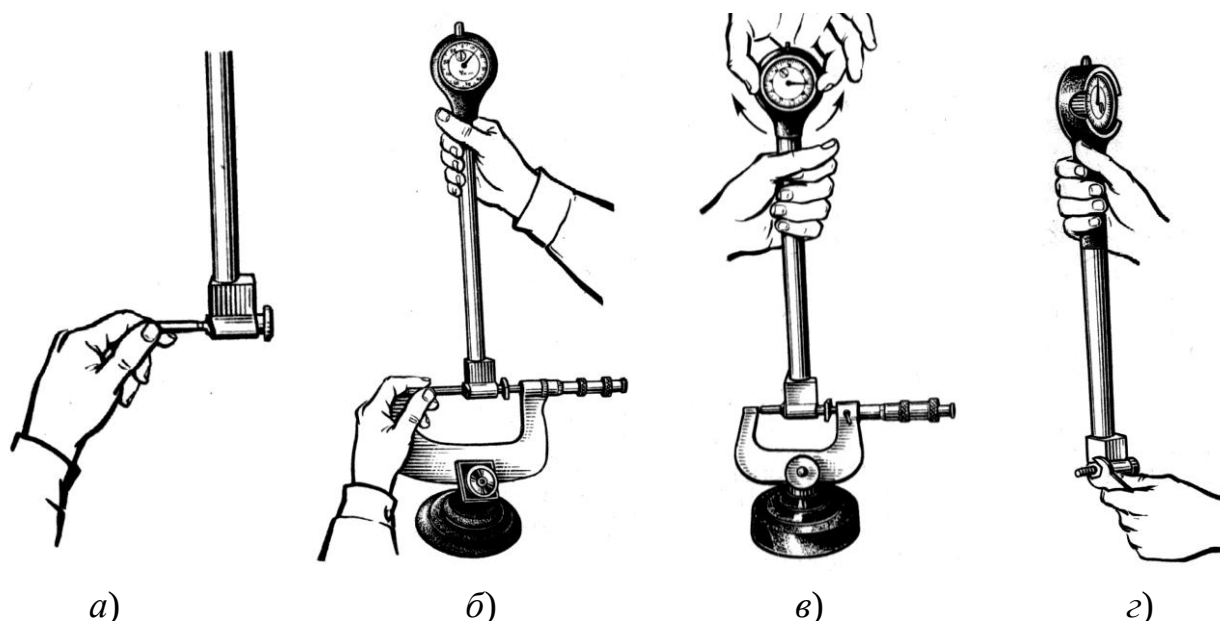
Схема выставления установочного размера индикаторного нутромера
